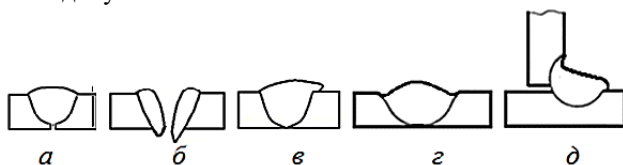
Типичные наружные дефекты сварных швов
